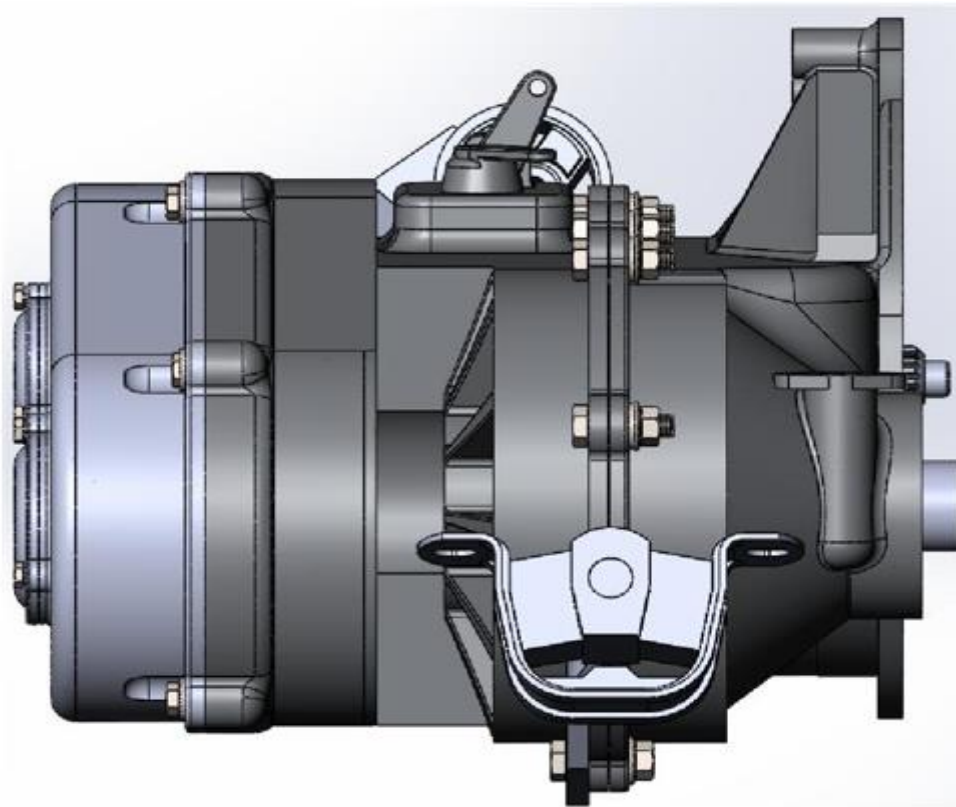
Бесступенчатая коробка передач (вид слева)
